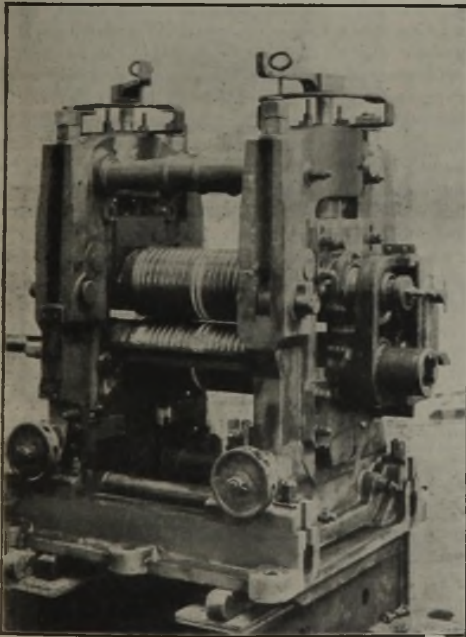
Walzgerüst mit Schlepplwalzenantrieb.
